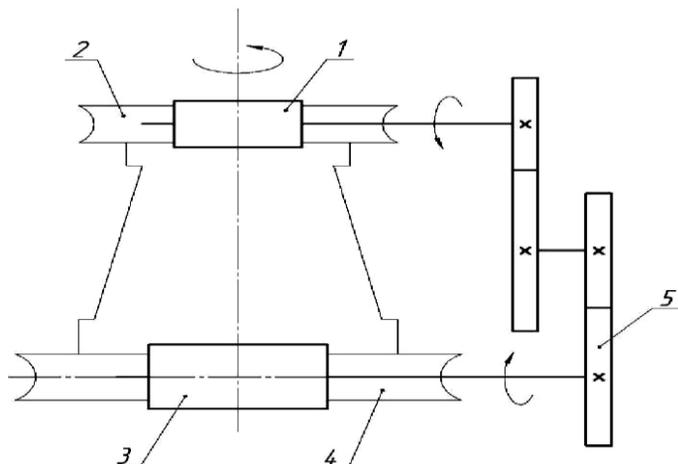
Цепь обката зуборезного станка: 1- червяк; 2- нарезаемое колесо; 3- червяк; 4- червячное колесо; 5- сменные колеса гитары обката
